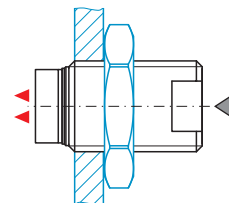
Zylindrische Sensoren mit Gewinde und Buchse
